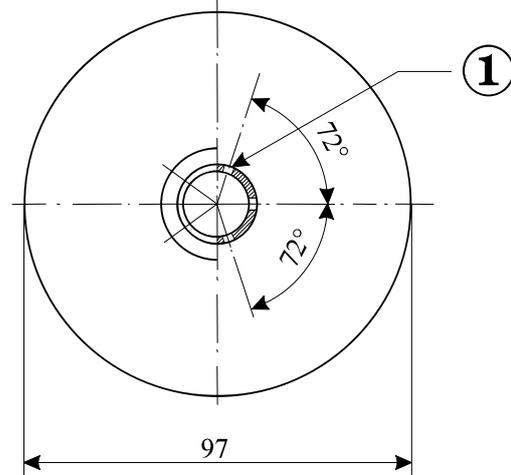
Hohler Bronzeyylinder, einseitig verschlossen.
